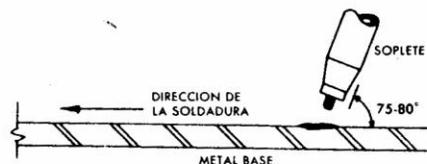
Manera de correr un cordón sin varilla de soldadura.
